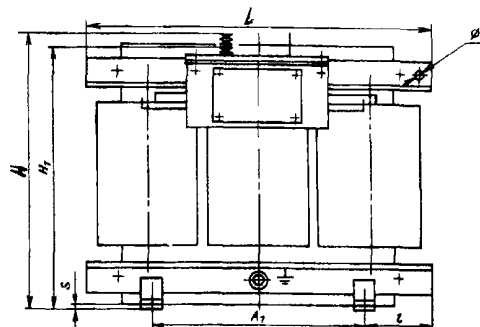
Габаритные, установочные, присоединительные размеры трансформатора ТСП
